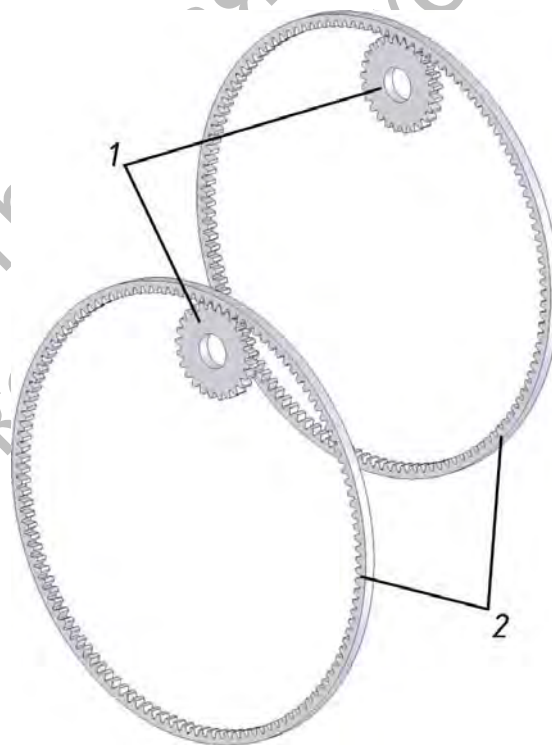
Общий вид компьютерной модели эвольвентной цилиндрической передачи с передаточным отношением 25: 1 – шестерня; 2 – колесо
